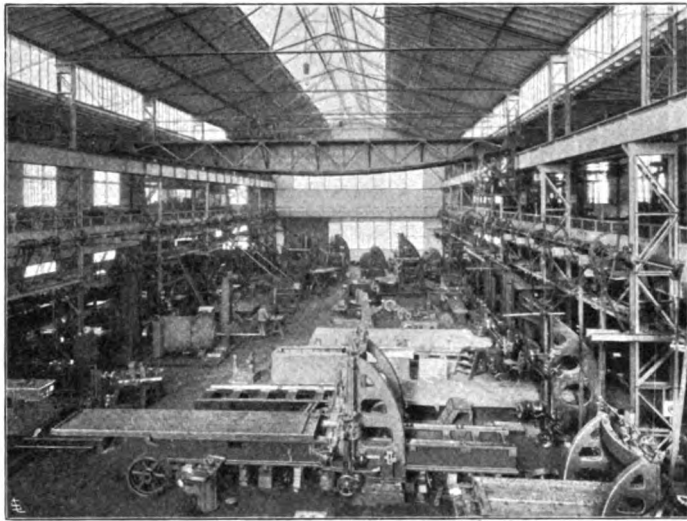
de Fries & Co., A.-G. Innenansicht der Montagehalle.
